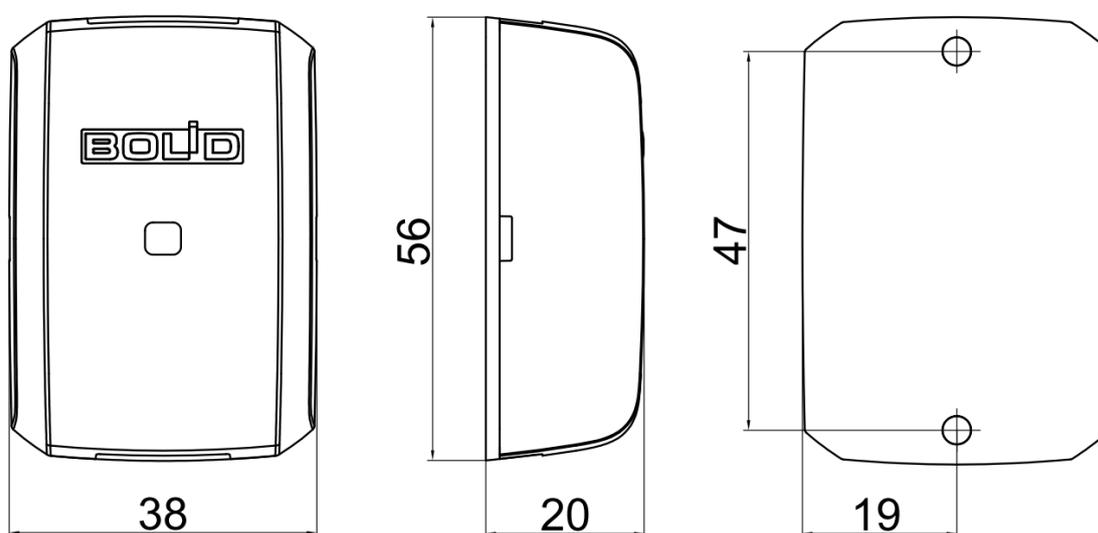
Габаритные и присоединительные размеры модуля Рупор-300-МК.
